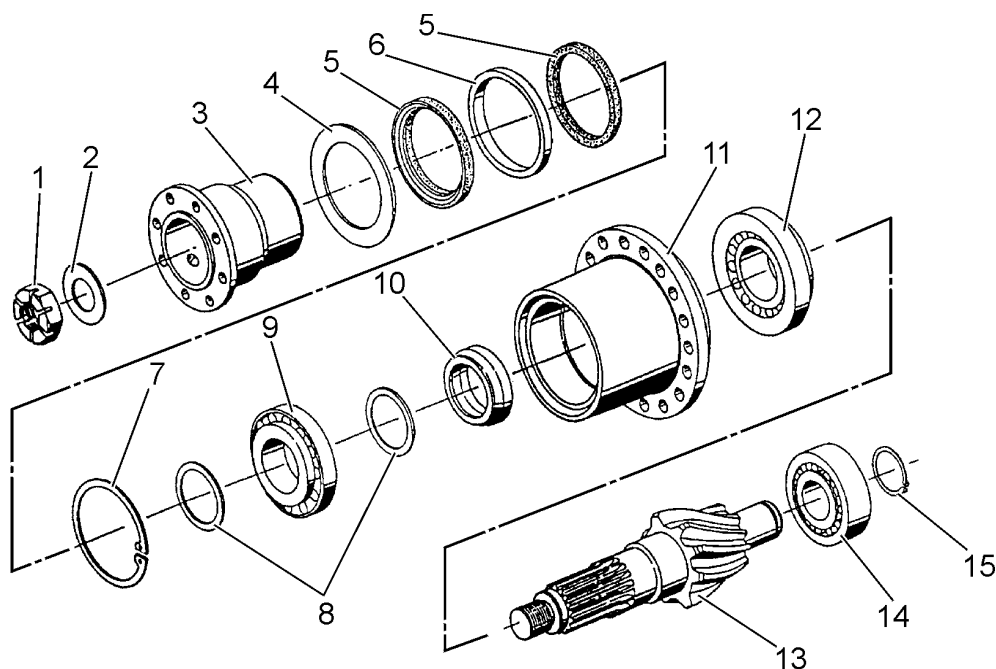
D.13. Узел вала ведущей шестерни (разборка)
